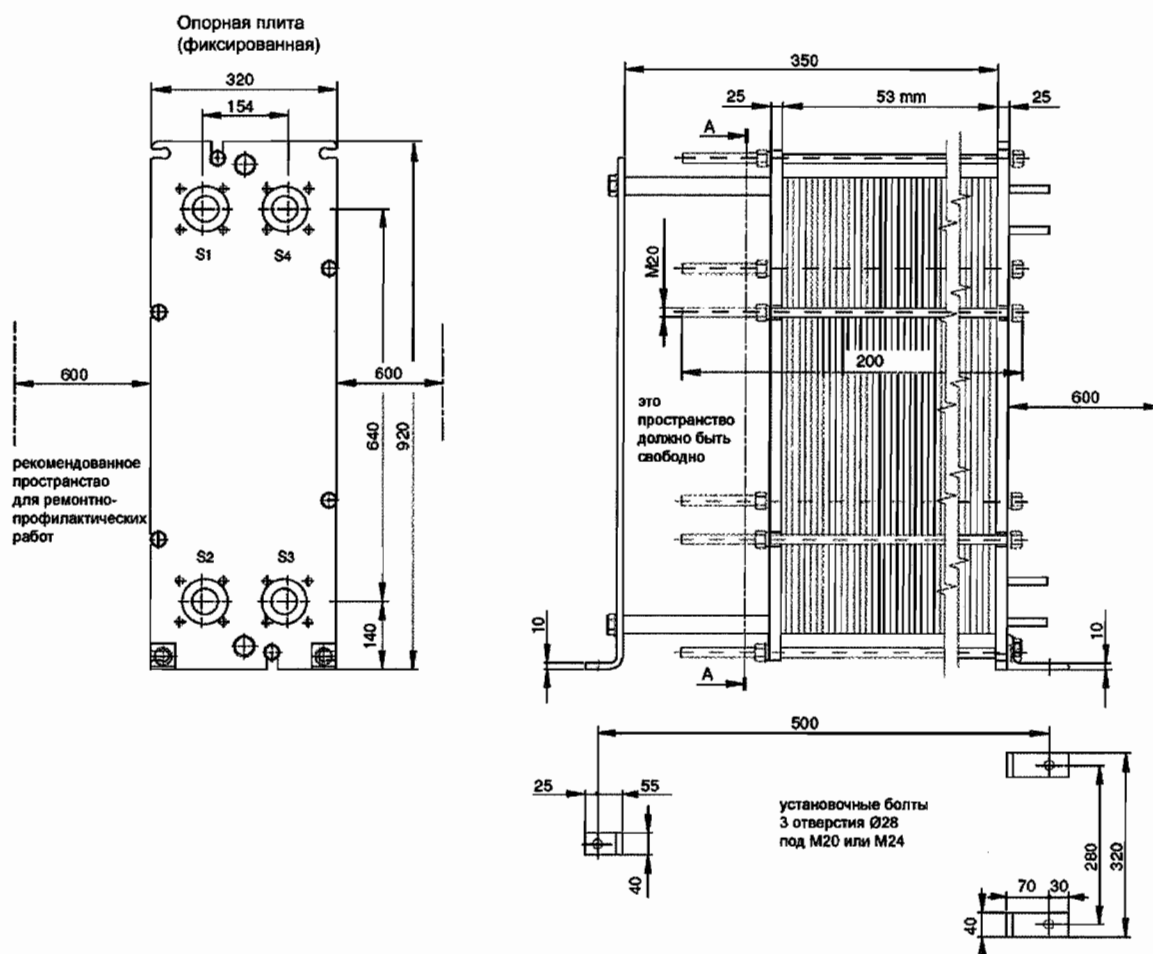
Габаритный чертеж охладителя борного концентрата KBF50AC001
